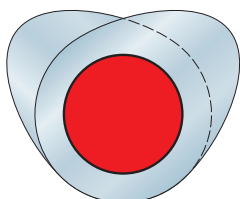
Положение кулачков первого цилиндра при укладке распределительного вала в опоры головки цилиндров.
